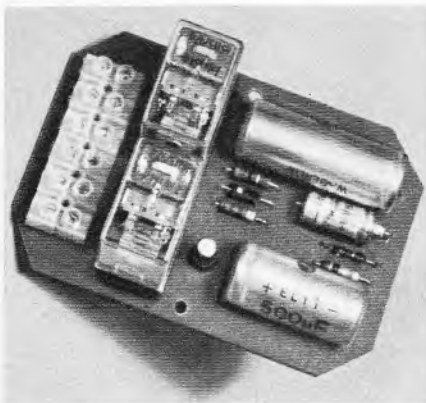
Das Mustergerät in Printplatten-Technik bei abgenommener Schutzhaube
